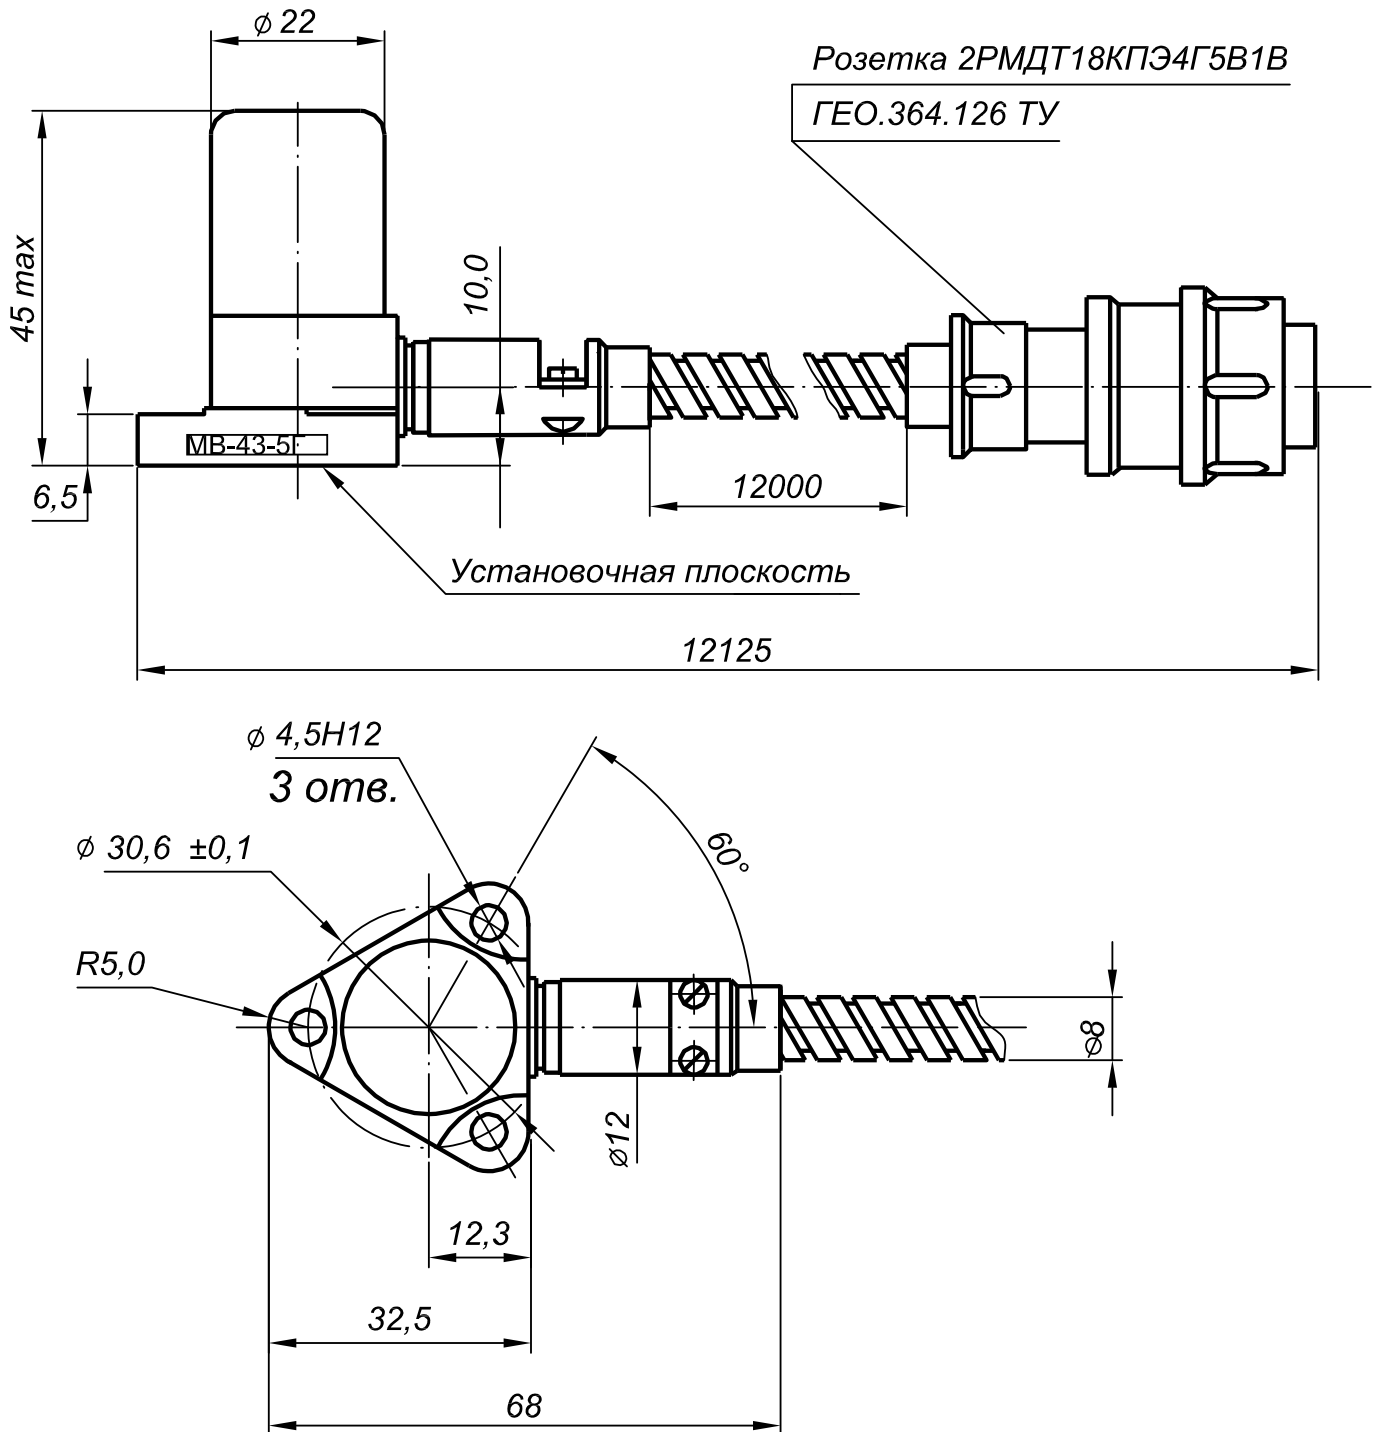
Габаритно-установочные размеры вибропреобразователя MB-43-5Г/12,0
